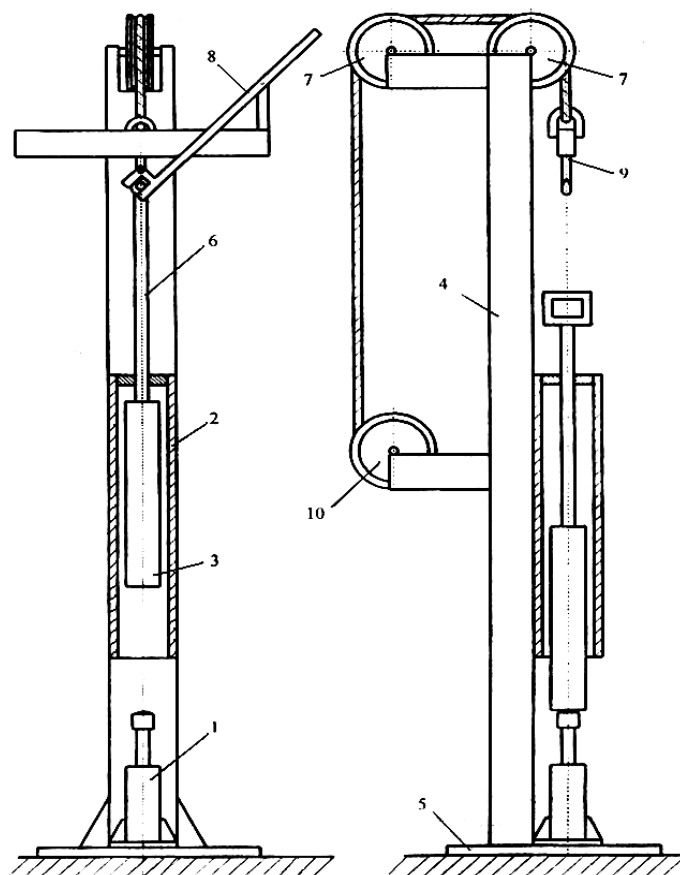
Установка для прессования керамических изделий падающим грузом [2], автор Тарасов В. Н.: 1 – пресс-форма; 2 – труба; 3 – груз; 4 – стойка; 5 – основание; 6 – штанга; 7 – блоки; 8 – рычаг; 9 – груз; 10 – лебедка
